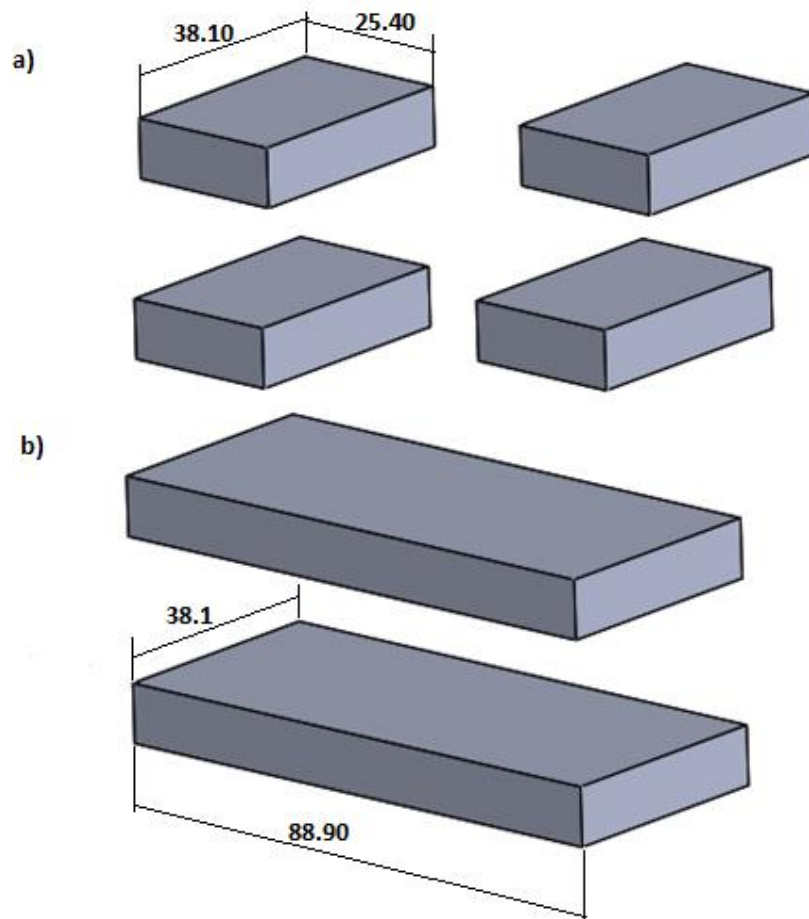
a) Secciones de pletina utilizadas para iniciar y finalizar cordón de soldadura, b) Secciones de pletina que formaran la probeta.
